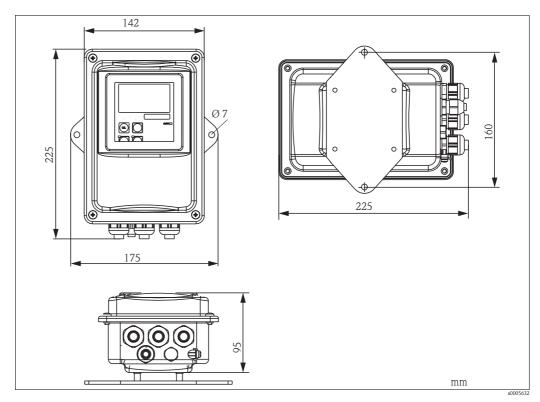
Montaje del CLD134 en una pared utilizando la placa de montaje
